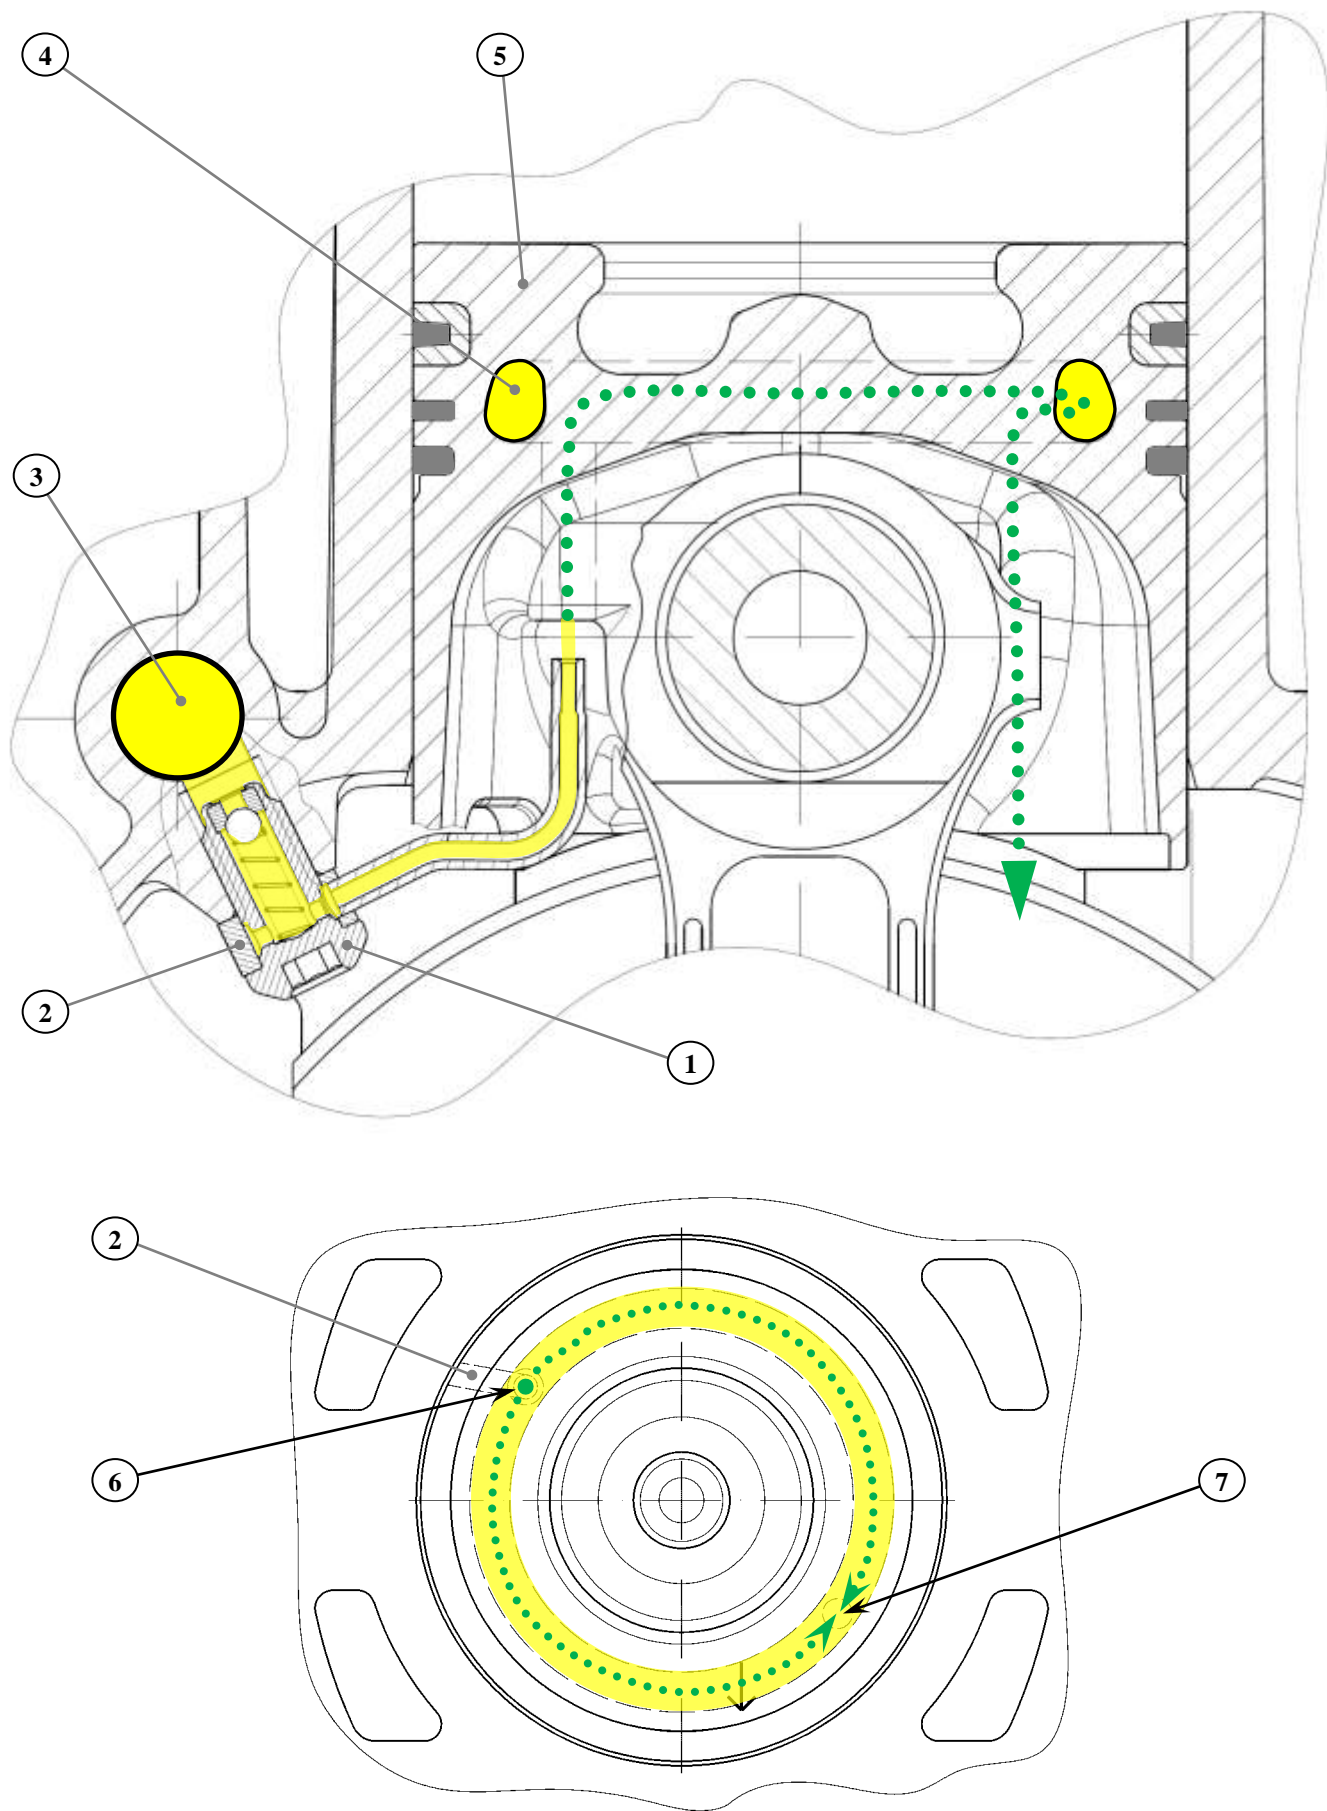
Схема подачи смазочного масла в канал охлаждения поршня:
